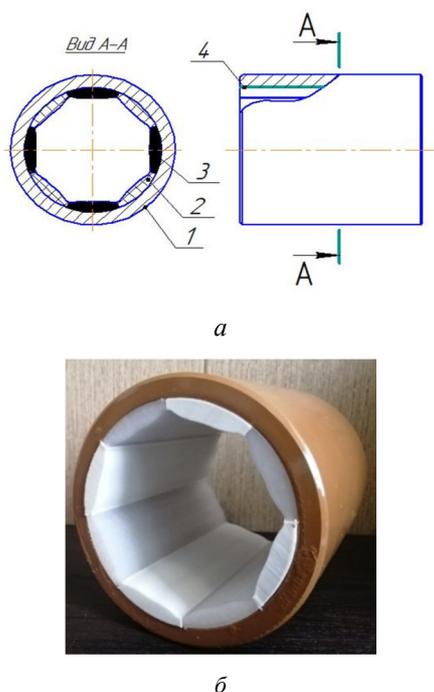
Комбинирование дейдвудного подшипника: а – конструкция дейдвудного подшипника: 1 – корпус; 2 – вкладыш из резины; 3 – вкладыш из материала ФУТ; 4 – клей; б – общий вид дейдвудного подшипника
